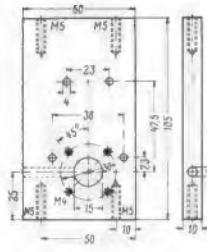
Rechte Seitenplatte, Aluminium 10 mm
